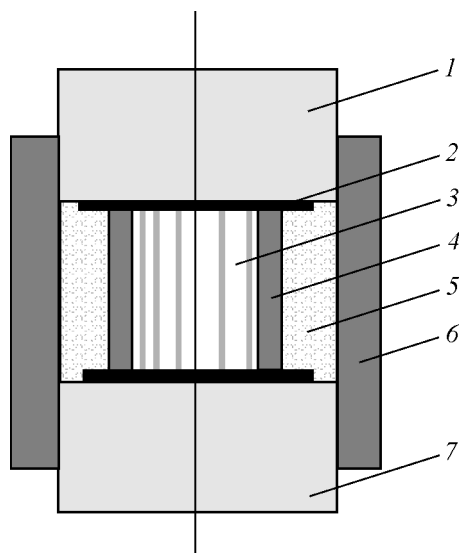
Схема сборки образца в контейнере-пакете для испытания образца на осадку
